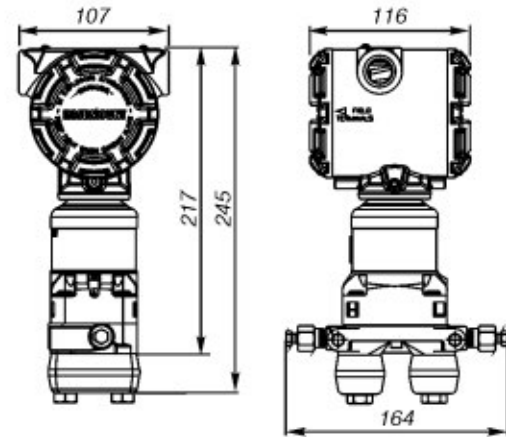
Корпус PlantWeb на платформе Coplanar SuperModule с фланцем Coplanar.
